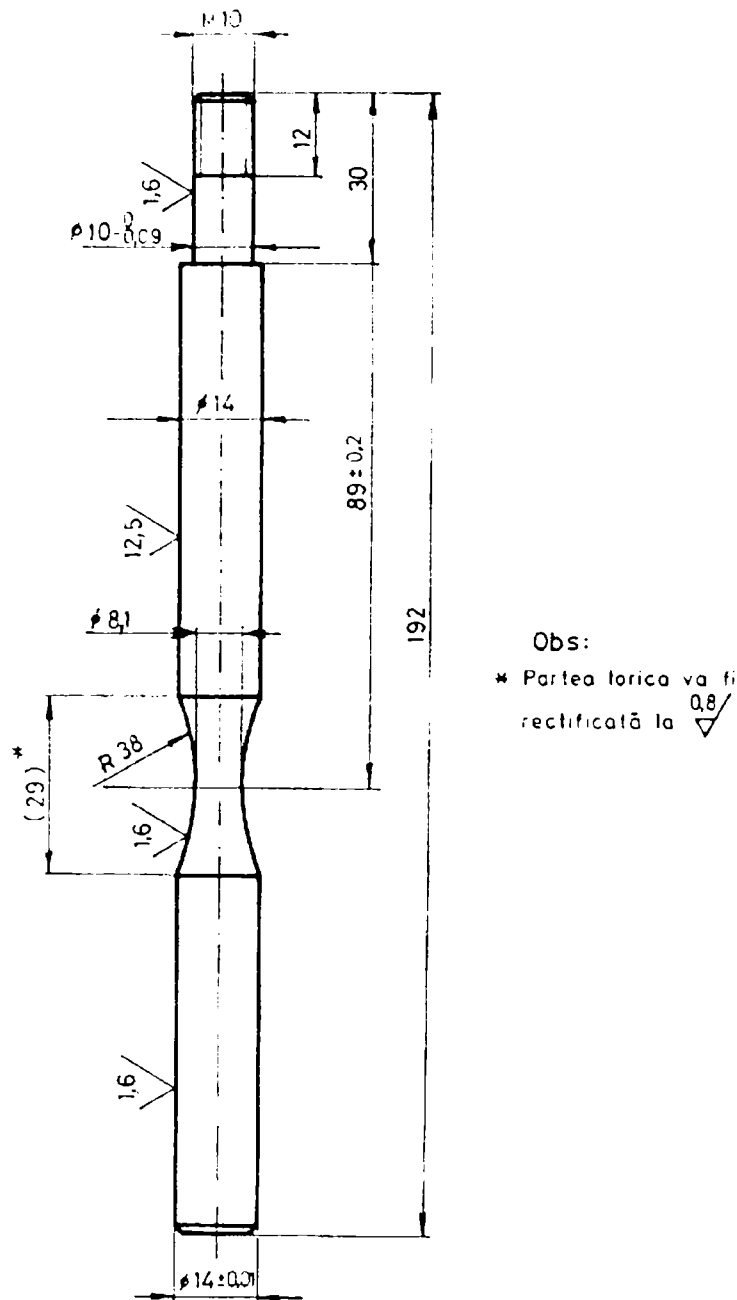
Epruveta de oboseală prin încovoiere rotativă
